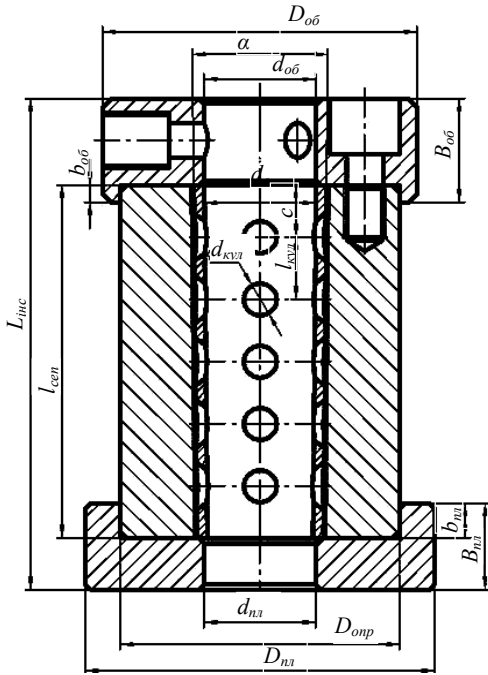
Пристрій для оброблення напівкруглих канавок шліцьових валів
